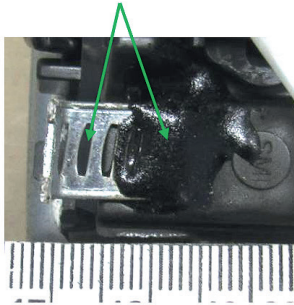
Загальний вигляд внутрішніх поверхонь та механізмів лічильника газу "Ельстер G4" та місця розташування металевої пластини з нашаруванням полімерної речовини чорного кольору (вигляд зверху)
